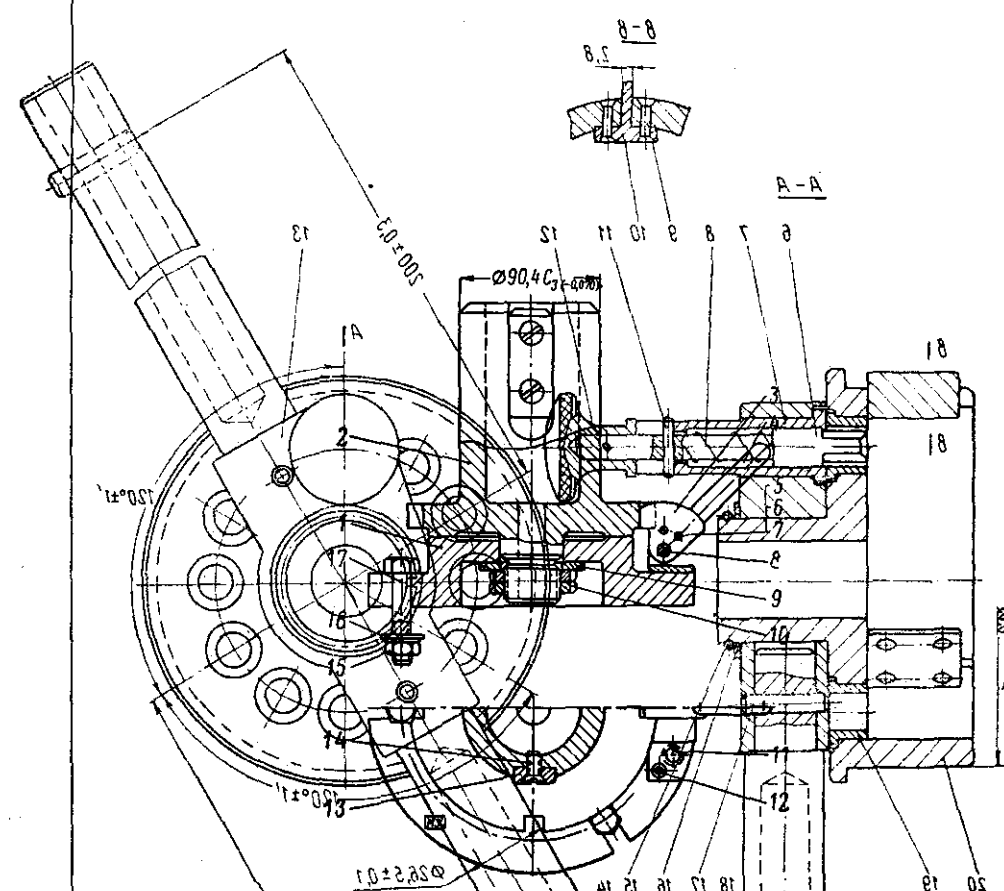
Приспособление 63509/806 для разборки узла корпуса и подбора натяга:
